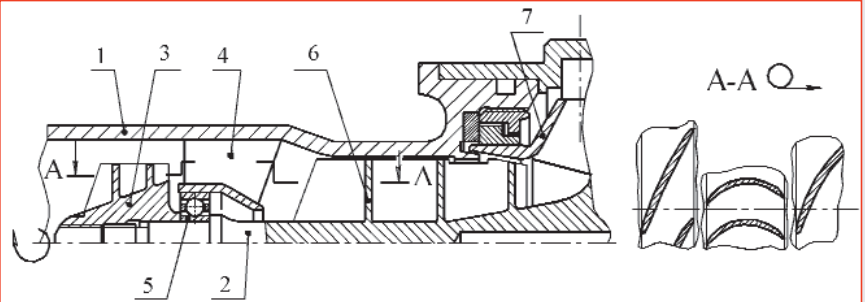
1 - корпус насоса, 2 - вал, 3 - бустерный шнек, 4 - пилон, 5 - подшипник, 6 - предвключенный шнек, 7 - центробежное колесо
